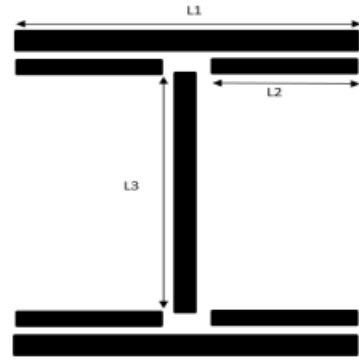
Assemblage soudé poutre- platine.
